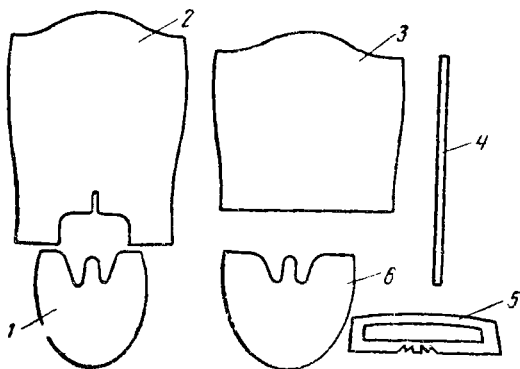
Детали заготовки юфтевого прикройного сапога:
